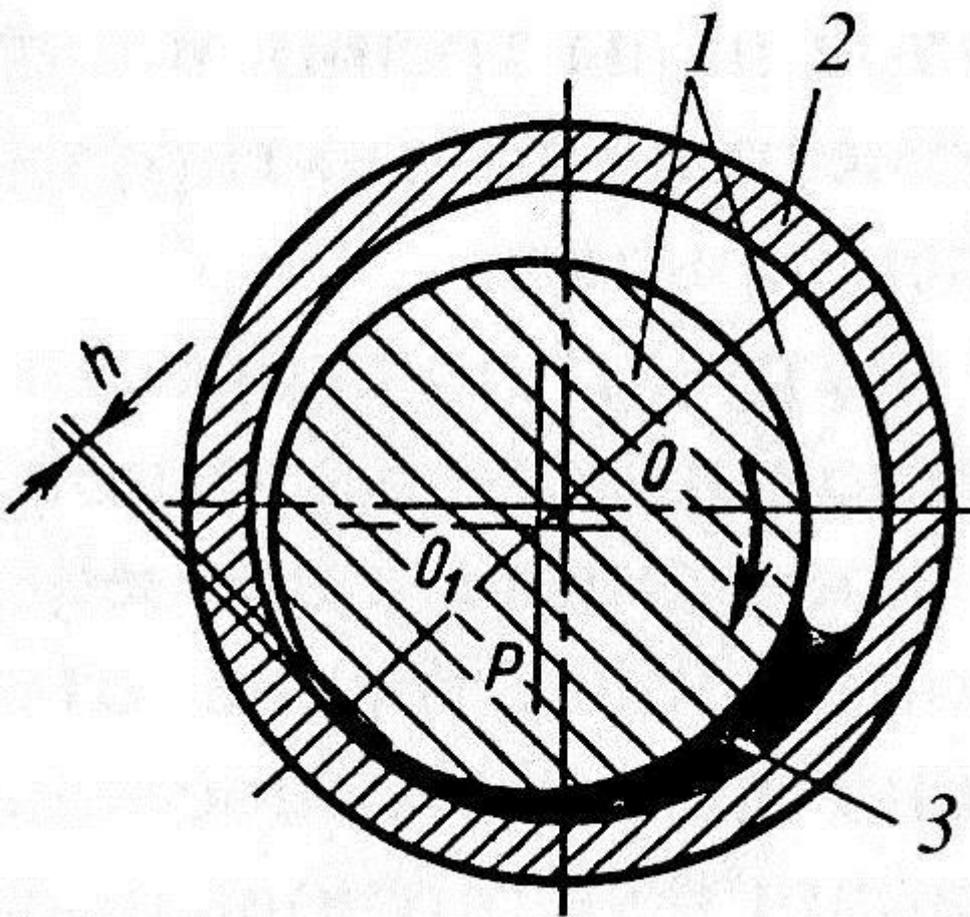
Схема образования несущей способности масляного слоя: 1 – шейка вала, 2 – подшипник (втулка), 3 – масляный клин; 0 – центр втулки, O_1 - центр шейки вала, h – толщина слоя смазки
